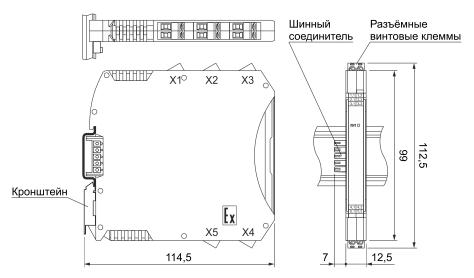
Габаритные размеры барьера KA5132Ex-N0 (шинный соединитель не мешает установке барьеров вплотную друг к другу)
